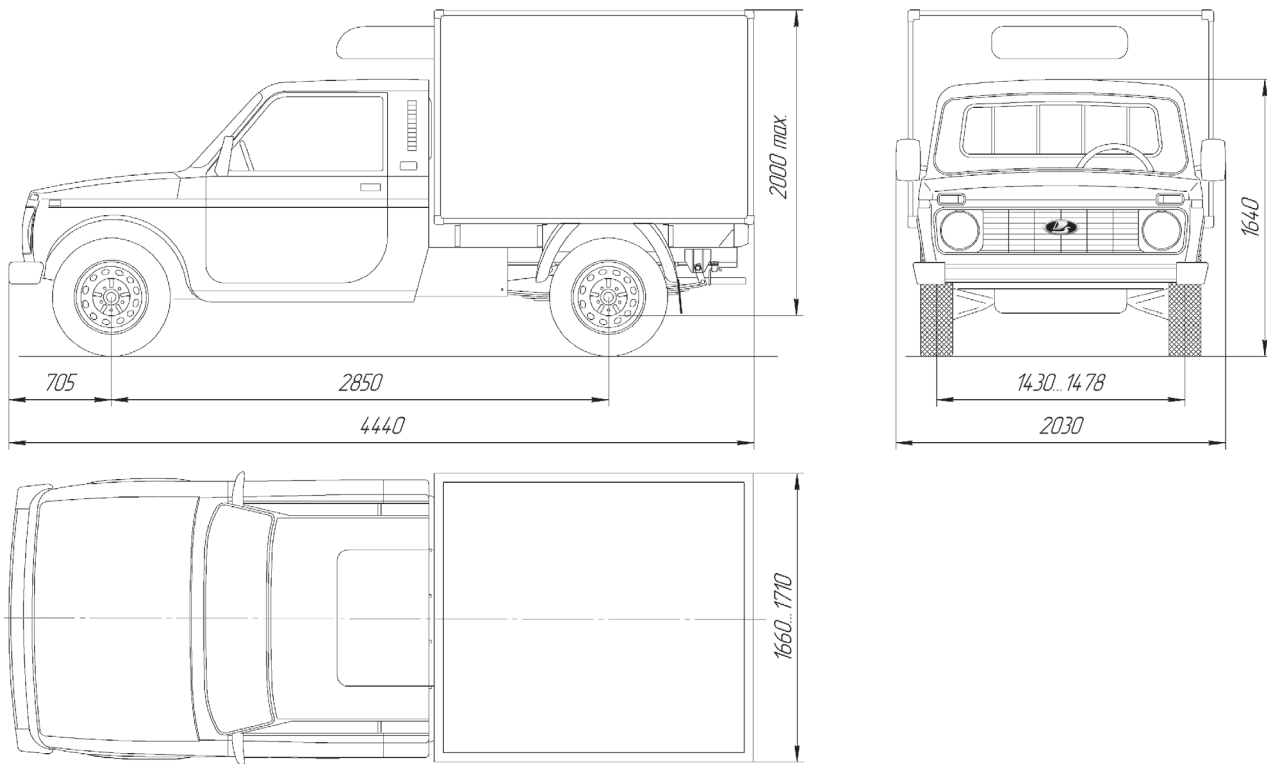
Габаритные размеры автомобиля ВИС-234600 (в исполнении с рефрижератором)
